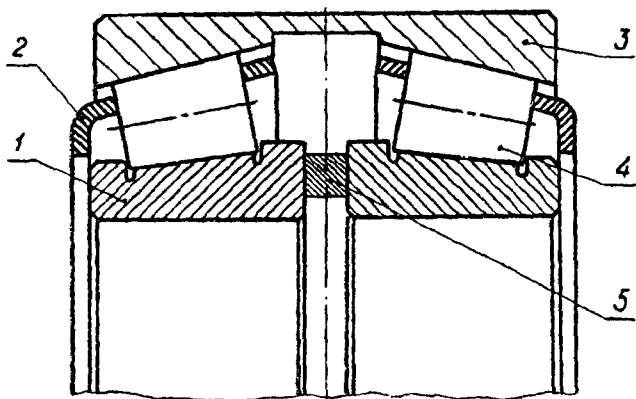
Двухрядный роликоподшипник с коническими роликами
